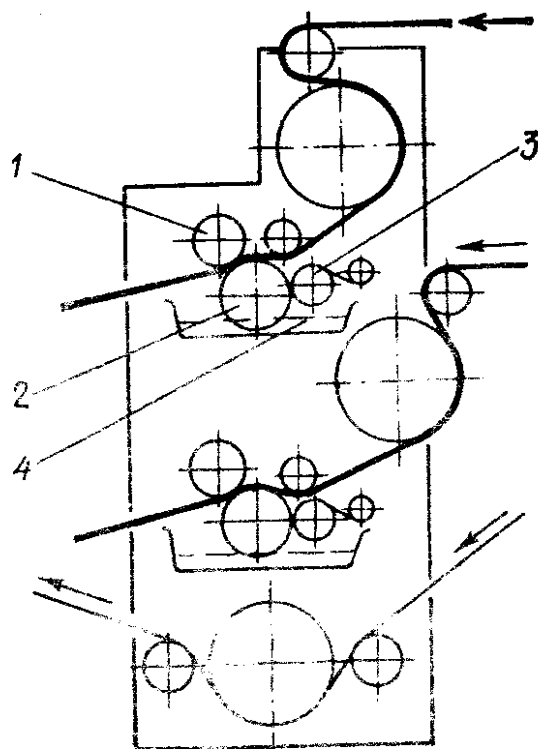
Двухъярусное клеильное устройство: 1 – прижимной подхватывающий валик; 2 – клеенаносящий валик; 3 – шаберный
